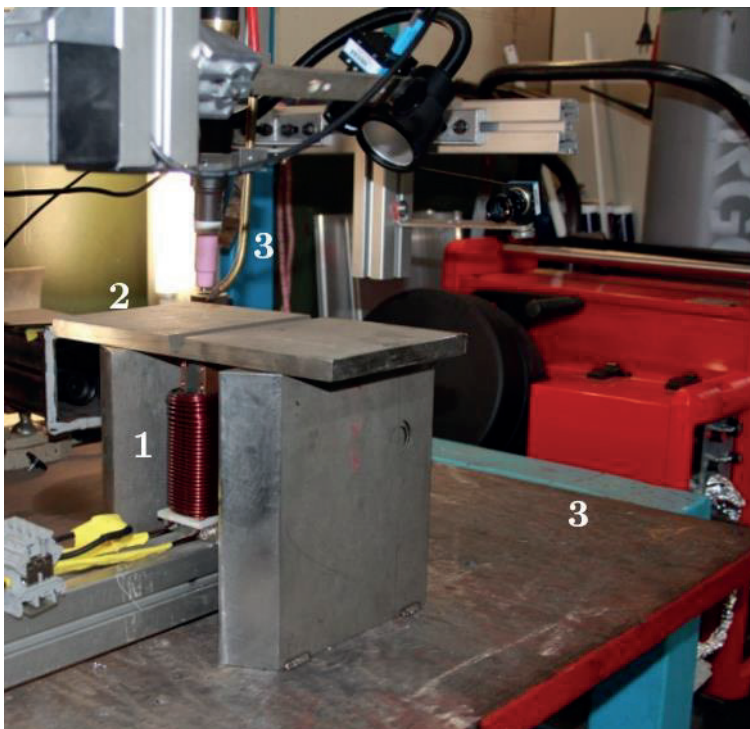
Schweißplatzaufbau: 1) Elektromagnet unter einer 2) vorerodierten Probenplatte auf
